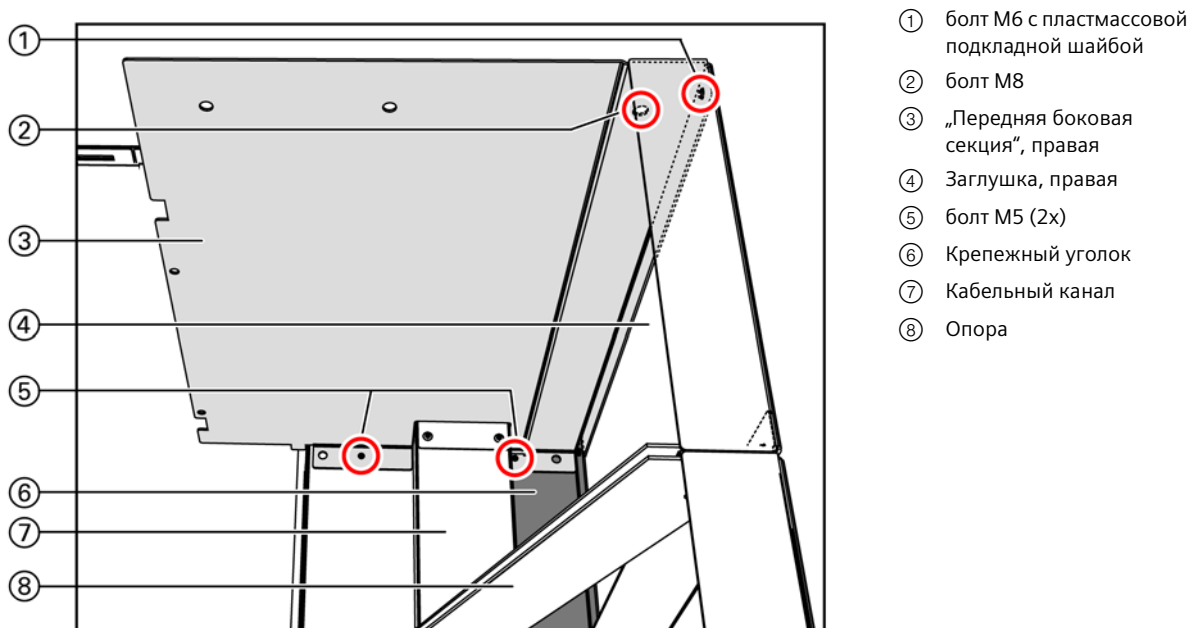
Точки крепления „передней боковой секции“ на резервуаре ячейки и на заглушке (вид изнутри правой стороны устройства)
